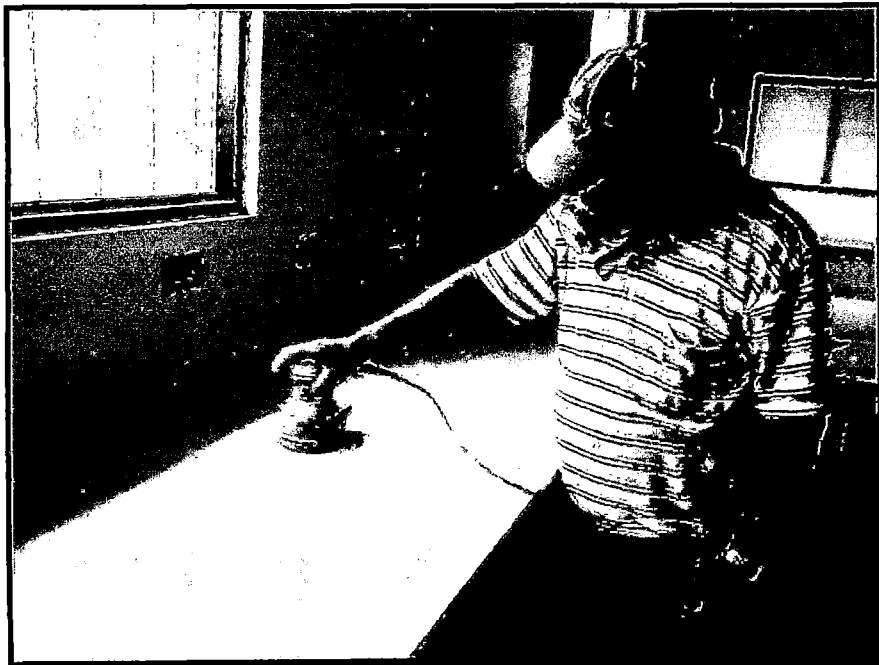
El siguiente proceso es realizar el boleado en la intersección de las planchas que han sido pegadas. En el detalle 1 se observa la unión vertical de los mandiles y en el detalle 2 se observa la intersección horizontal entre dos planchas que conforman la mesa.
